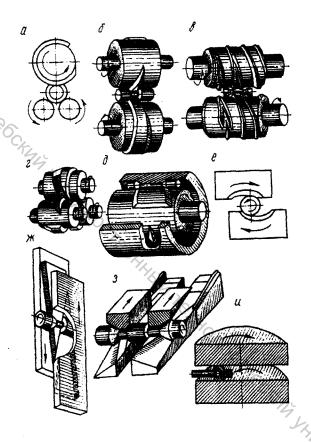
Схемы станов поперечно-клиновой прокатки:
